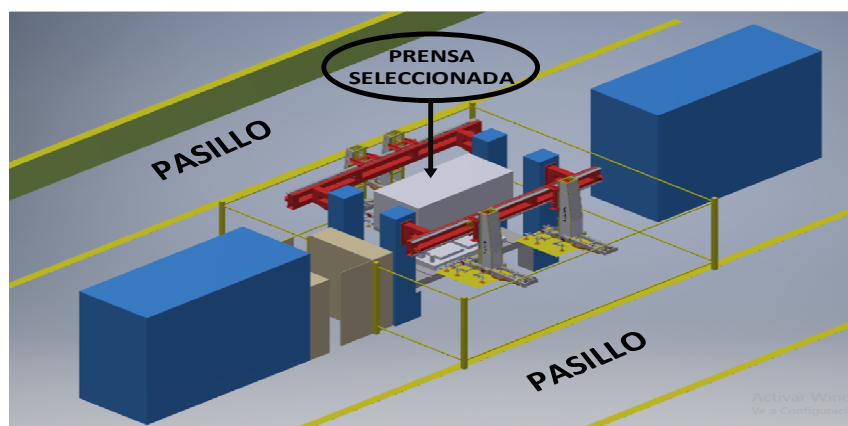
Layout del área de trabajo de la prensa excéntrica CALININ.
